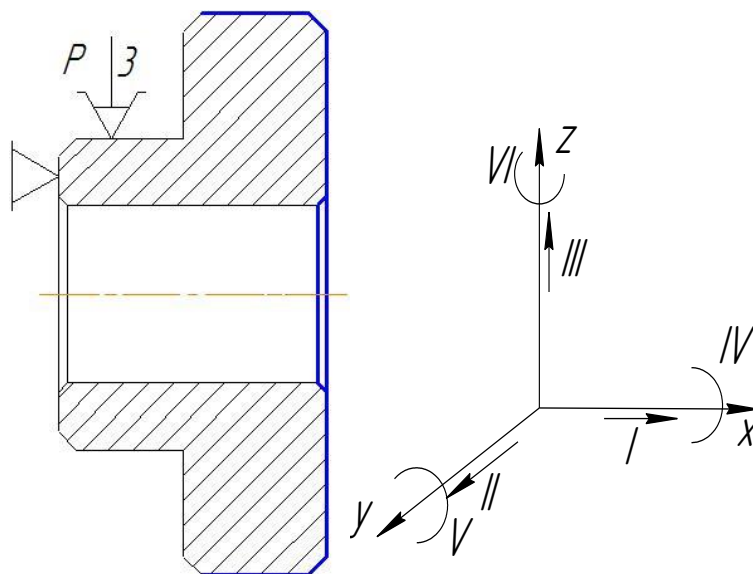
Схема базування заготовки на токарно-багаторізевої операції
